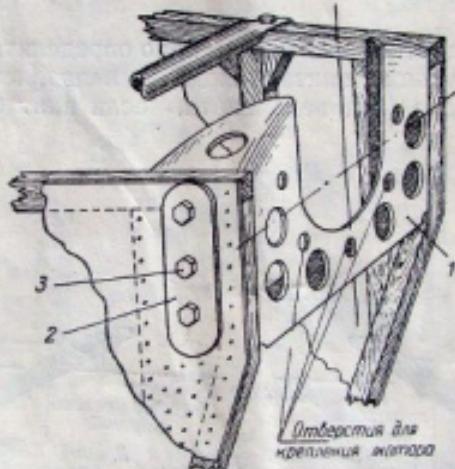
Рама для крепления двигателя двухместных аэросаней конструкции Коростылева
